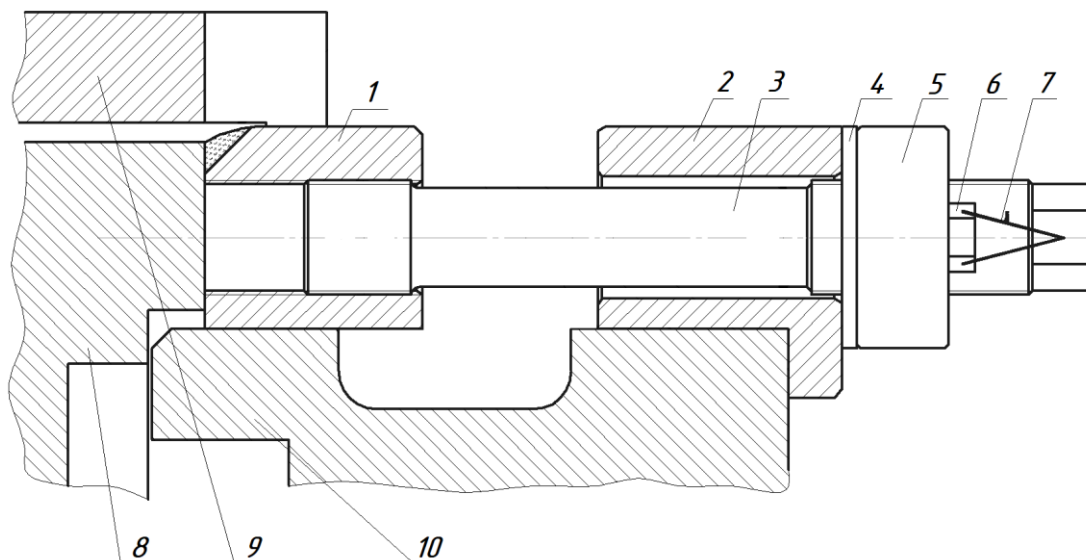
Фрагмент системи кріплення осердя статора (1 – бонка; 2 – упор; 3 – шпилька; 4 – проліжка; 5 – гайка; 6 – болт; 7 – контровочний дріт; 8 – рама; 9 – корпус статора; 10 – фланець)
